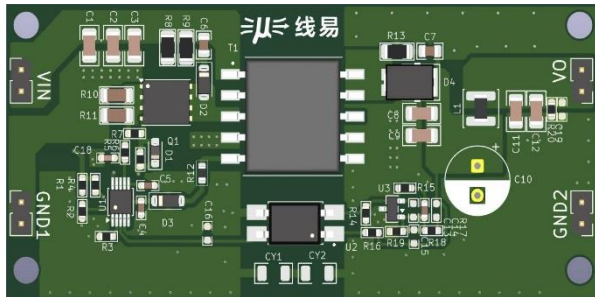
PCB 版图正面 (尺寸: 35x 75mm)
